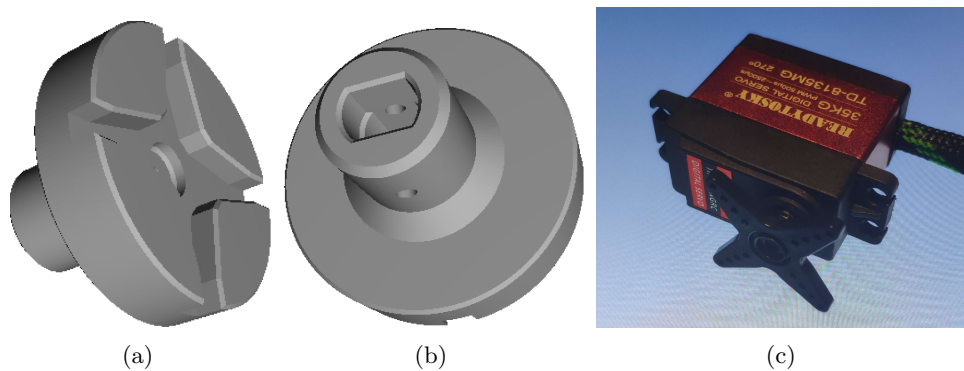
Adaptador entre o eixo da válvula e do motor (a) Visto de frente (b) Visto de traseira e, (c) Motor
